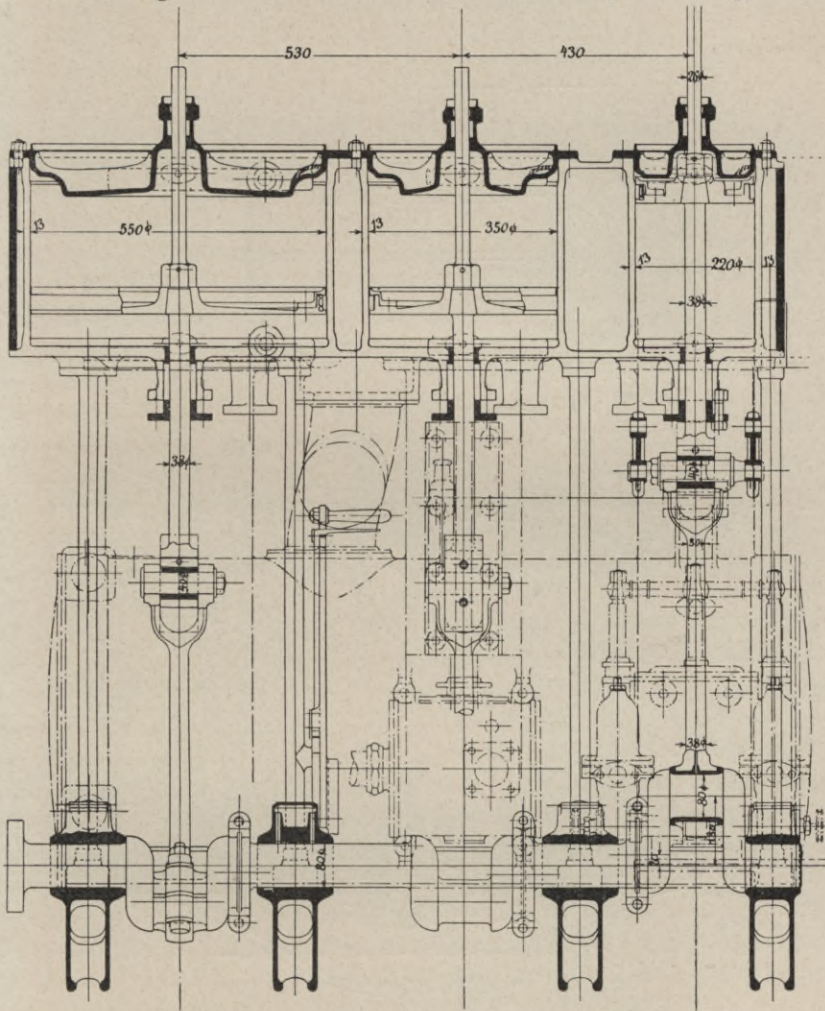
a. Dreifache Expansionsmaschine von Ziese.
